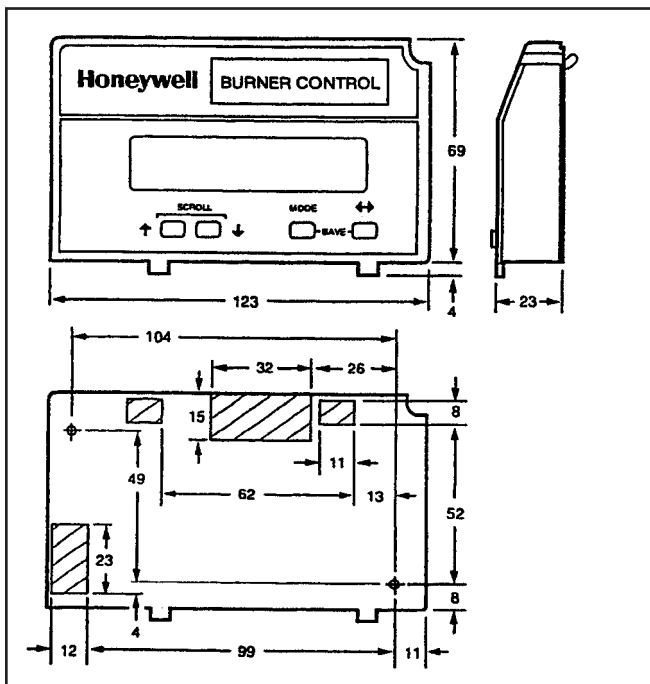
Encombrement en millimètres du module d'affichage à touches
